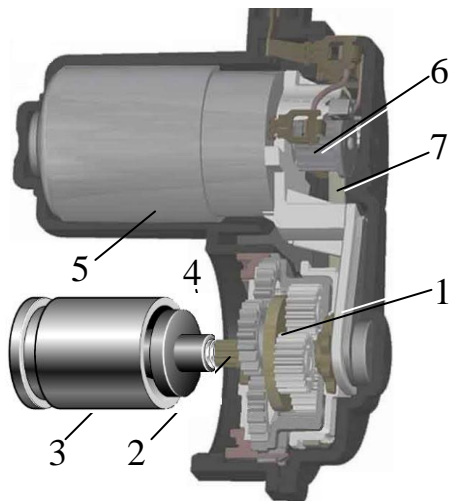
Привод электромеханического стояночного тормоза с планетарным редуктором: 1 – редуктор; 2 – выходной вал редуктора; 3 – поршень рабочей тормозной системы; 4 – винтовая пара; 3 – электродвигатель; 6 – выходной вал электродвигателя; 7 – зубчатый ремень
